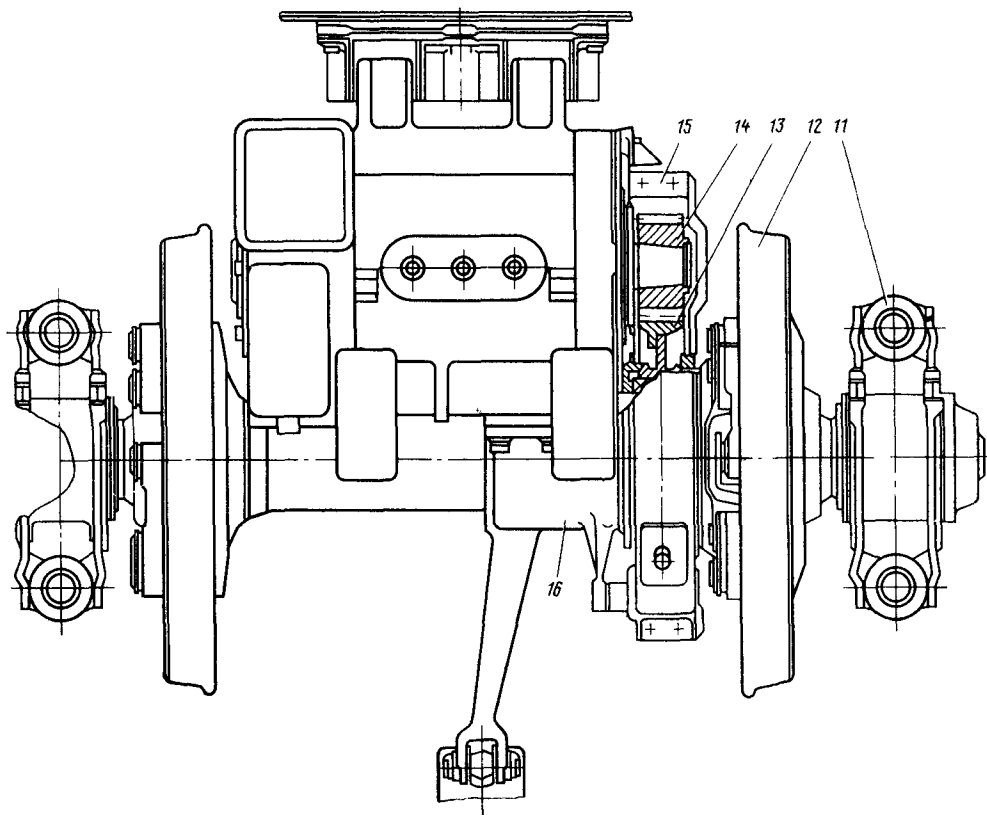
Колесно-моторный блок тепловоза ТЭП70:
